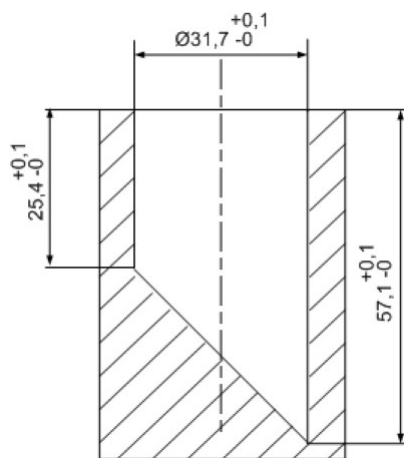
Cuerpo de ensayo piezas pequeñas (dimensiones en mm)
